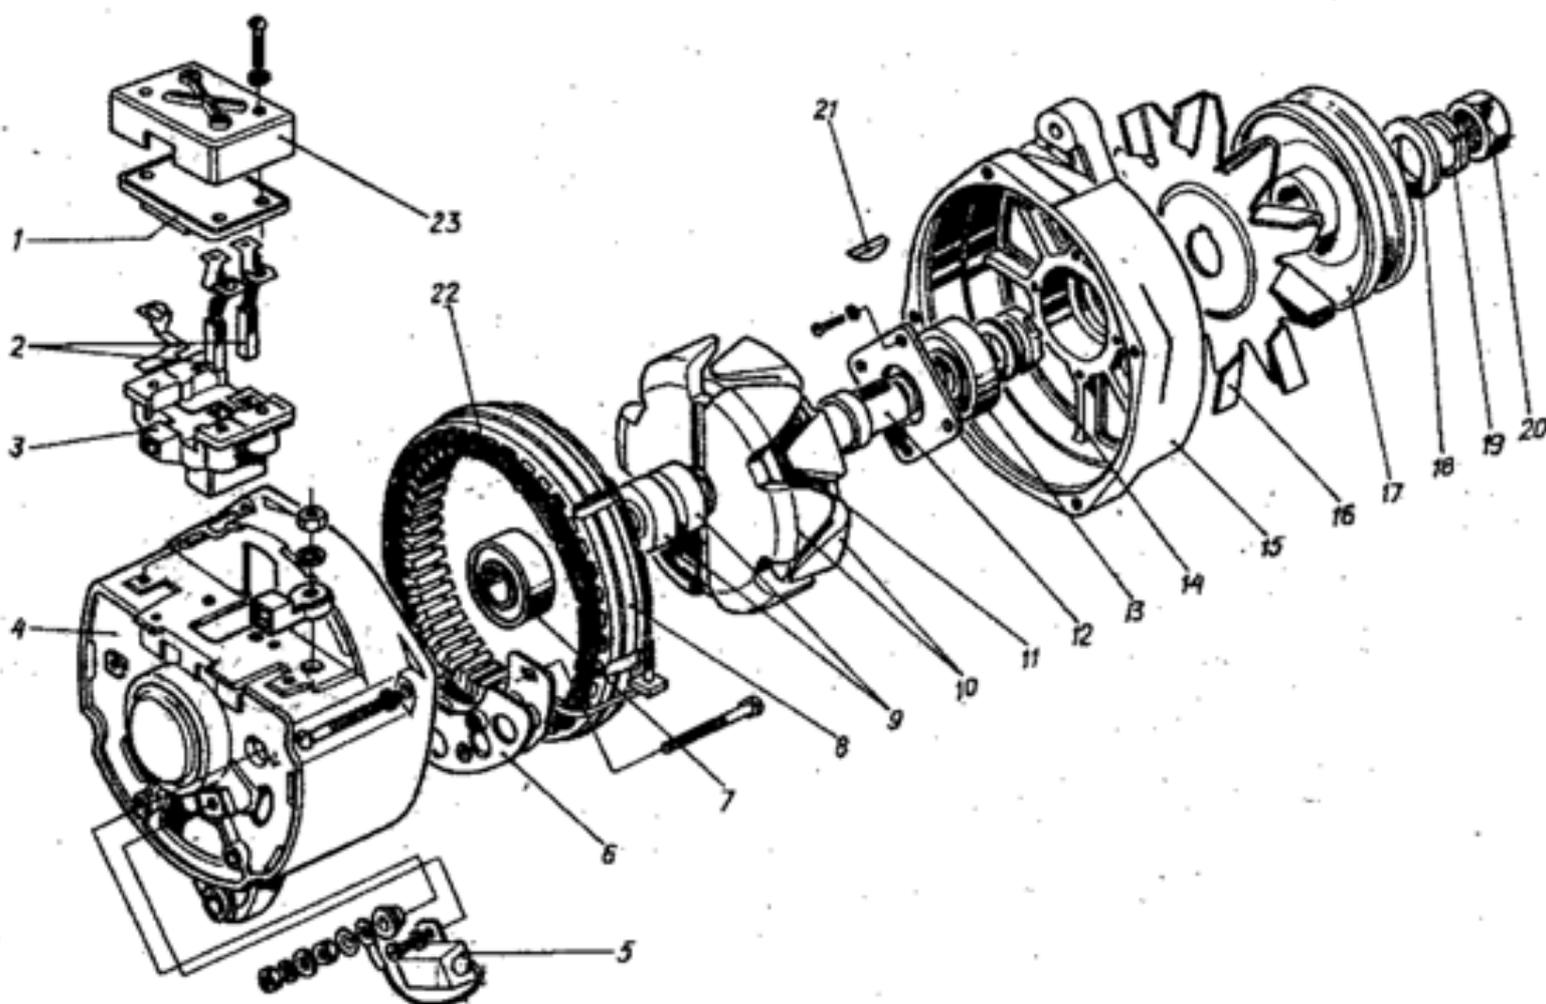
Детали генератора 583.3701: 1 - регулятор напряжения интегральный; 2 - щетки; 3 - щеткодержатель; 4 - крышка со стороны контактных колец; 5 - конденсатор; 6 - выпрямительный блок; 7 - подшипник; 8 - статор; 9 - контактные кольца; 10 - полюсные наконечники ротора; 11 - катушка возбуждения; 12 - вал ротора; 13 - подшипник; 14 - втулка; 15 - крышка со стороны привода; 16 - вентилятор; 17 - шкив; 18 - шайба; 19 - шайба стопорная; 20 - гайка; 21 - шпонка; 22 - обмотка статора; 23 - крышка регулятора напряжения;
